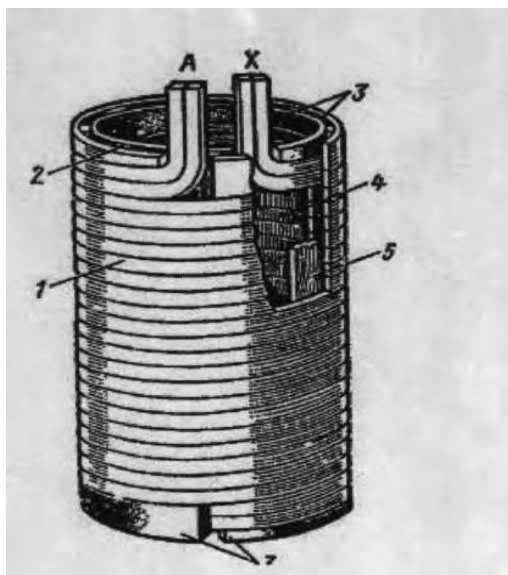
Двухслойная цилиндрическая обмотка с двумя параллельными проводниками:
